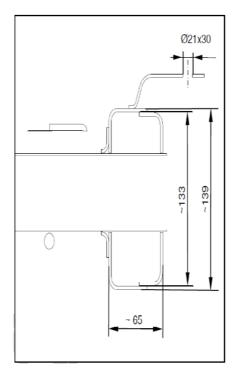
Sección R-R (Amarok SC/DC)
